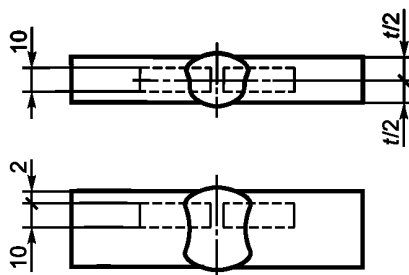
Расположение образцов для испытаний на ударный изгиб
